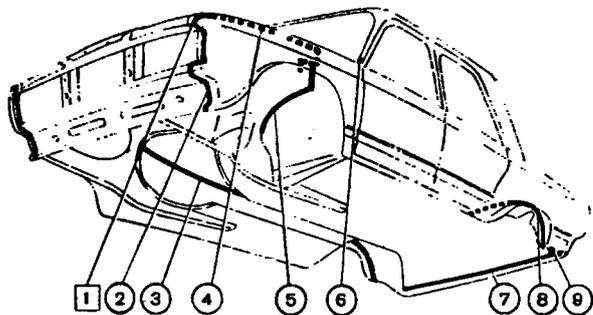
Сварные швы и стыки, на которые наносится уплотнительная мастика (вид кузова снизу): 1 - усилителя крыла с верхней поперечиной передка; 2 - переднего крыла с передней панелью передка; 3 - кожуха пола с полом; 4 - сточного желобка капота с передним крылом (с внутренней стороны крыла); 5 - брызговика с щитком передка; 6 - переднего крыла с рамой ветрового окна; 7 - нижней панели задка с задним полом; 8 - внутренней и внешней арок колес; 9 - полов запасного колеса и топливного бака с задними крыльями.
